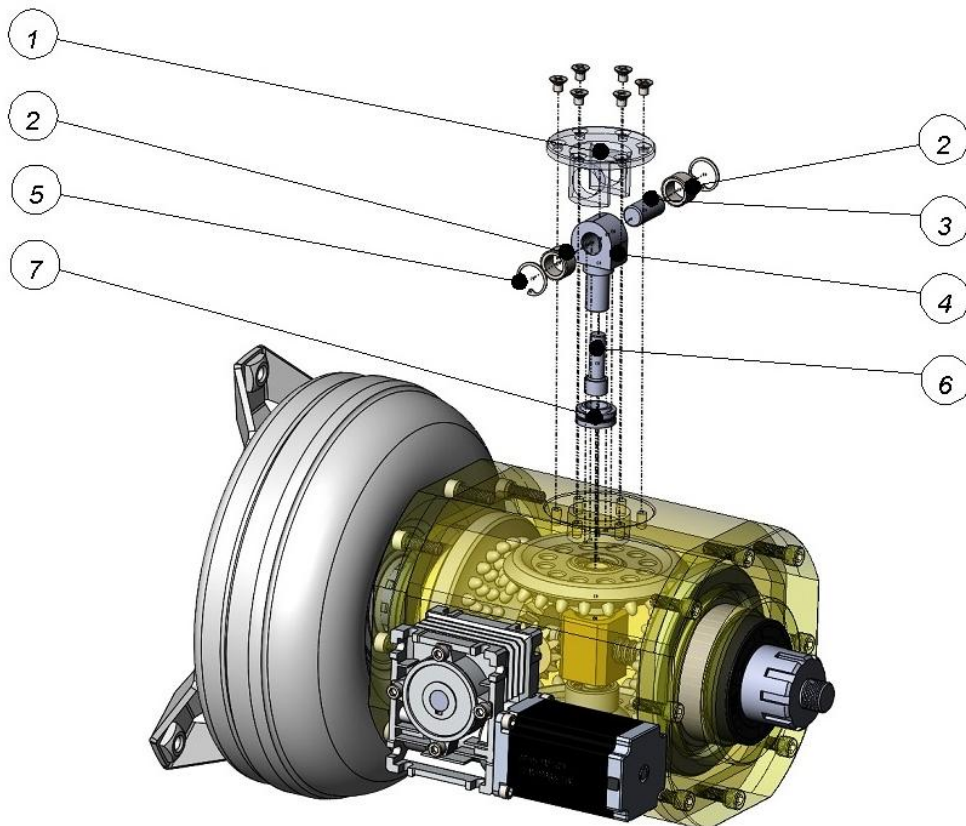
Будова механізму коливання сателітів: 1 – кронштейн; 2 – голкові підшипники; 3 – вісь коливання; 4 – кривошип; 5 – стопорні кільця; 6 – шток; 7 – підшипник типу ШС
